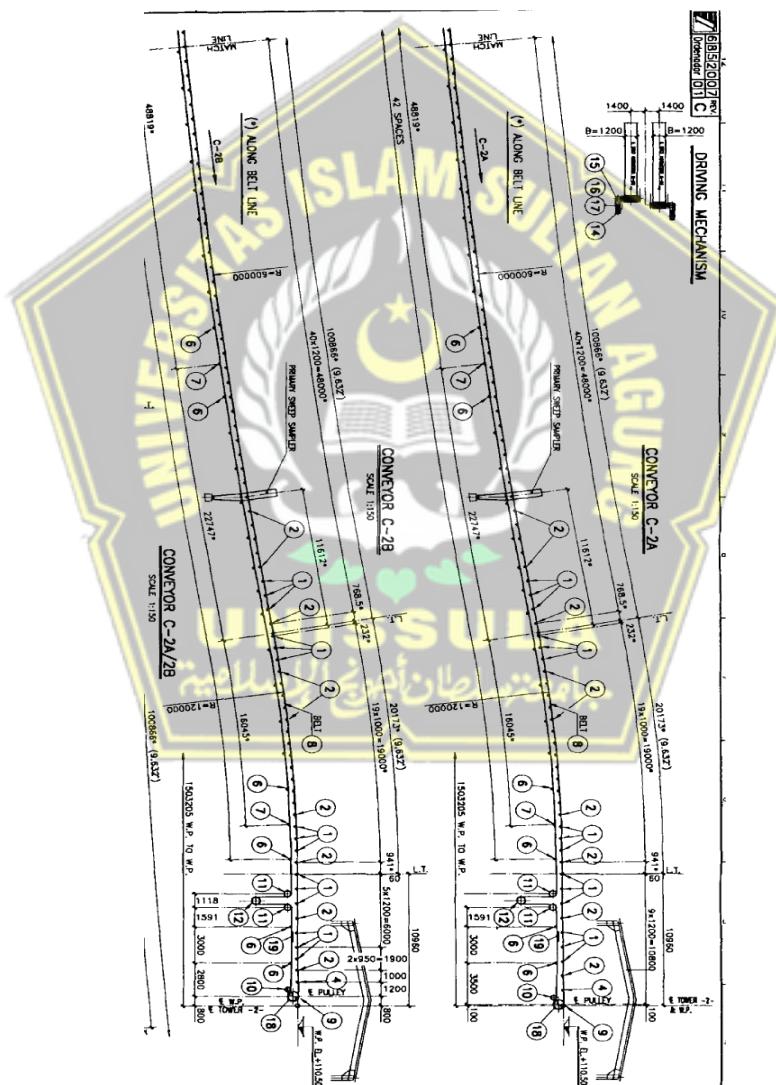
4. Drawing Conveyor 1A&B di PLTU Tanjung Jati B
